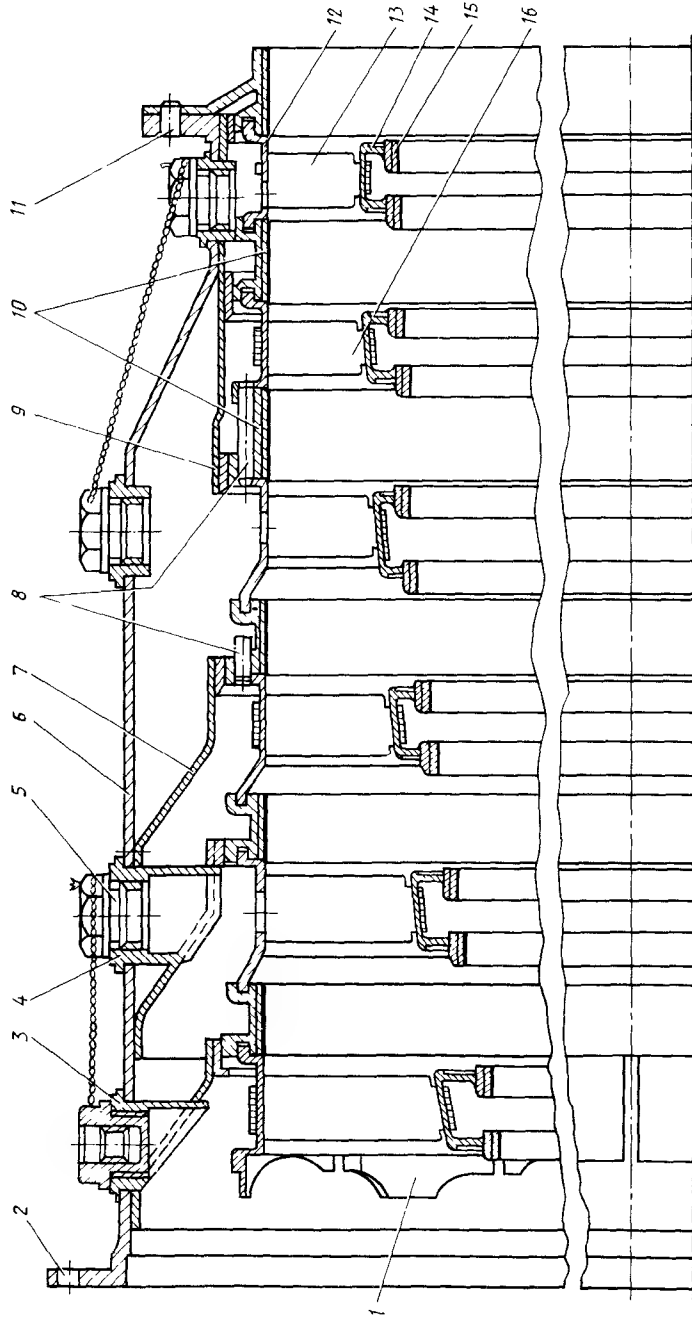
Корпус компрессора высокого давления ТРДД-36:
